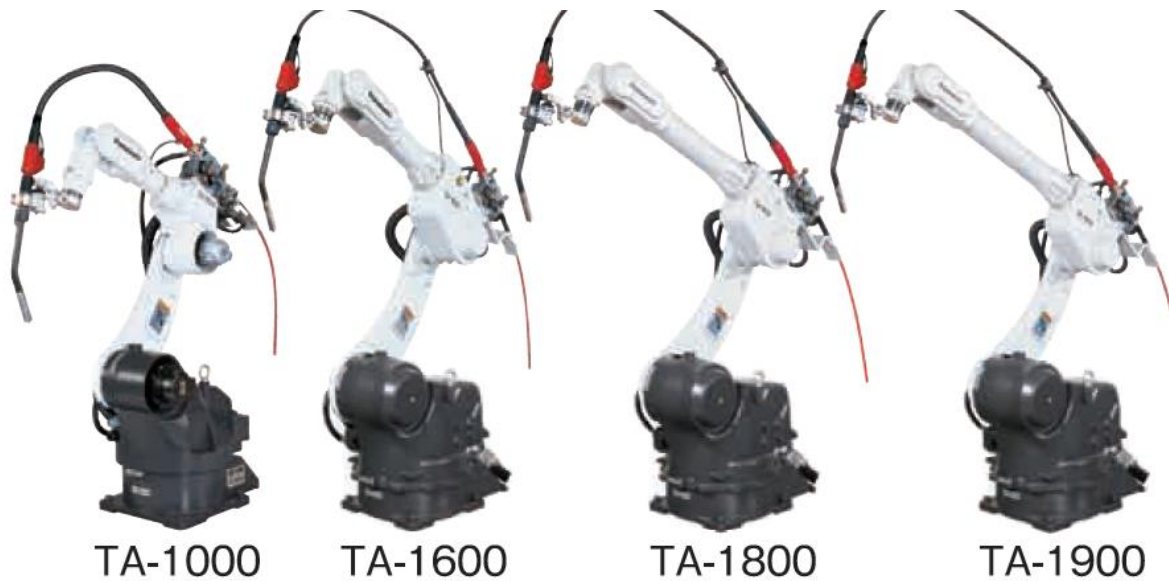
Robots marca Panasonic con equipo de soldadura Miller serie TA (MILLER, 2015)
